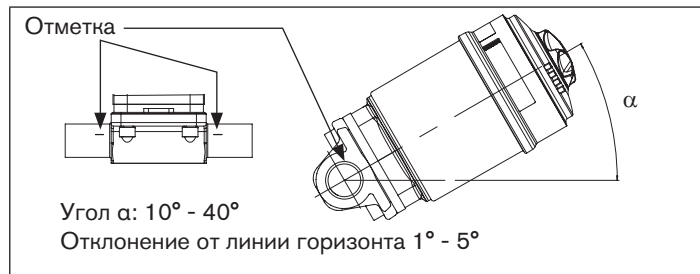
Положение при монтаже для самодренаживания корпуса клапана
